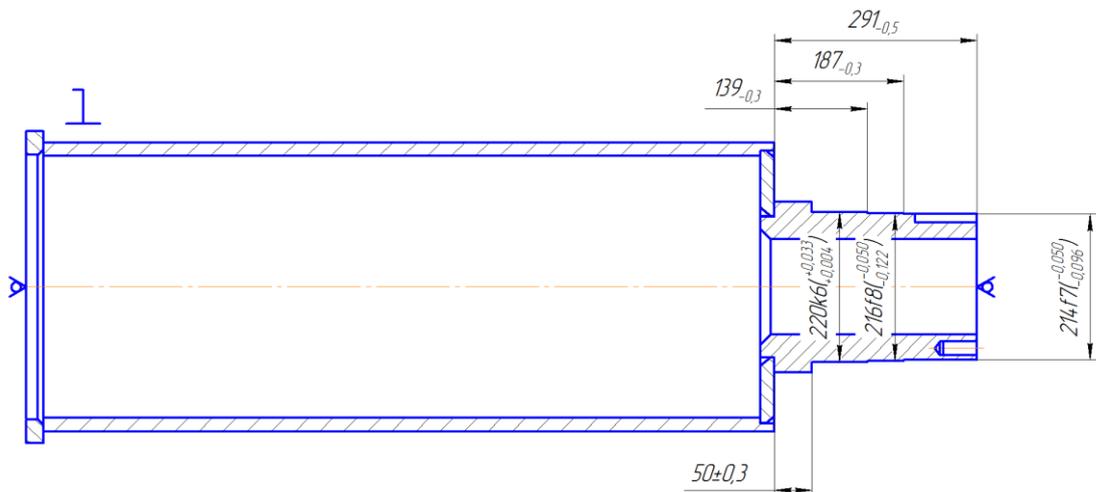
Эскиз базирования заготовки на 015 круглошлифовальной операции.
